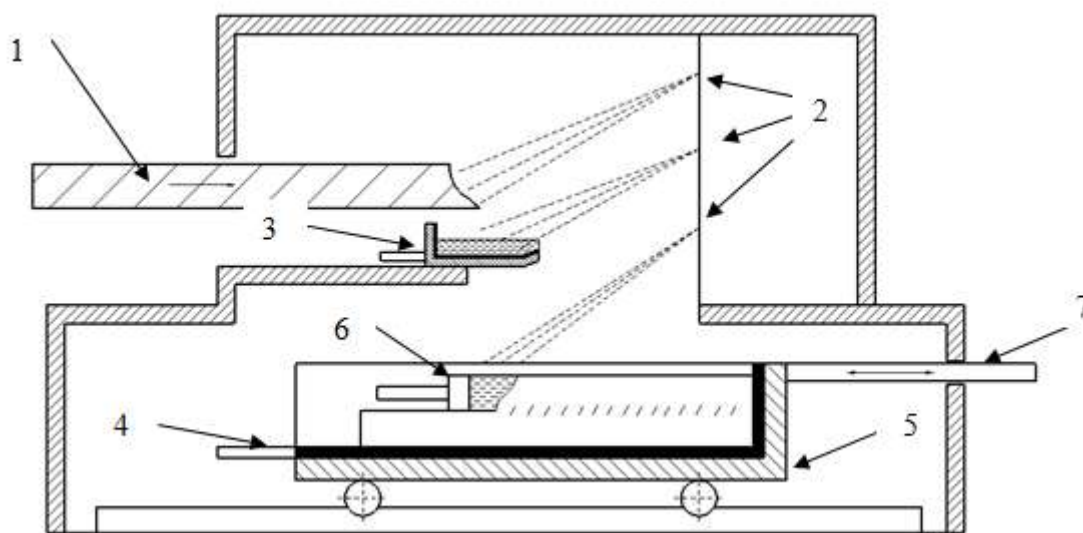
Схема установки для получения слитков: 1 – компактная заготовка или стружка; 2 – электронные пушки; 3 – промежуточная емкость; 4 – поддон; 5 – тележка; 6 – барьер; 7 – механизм перемещения
